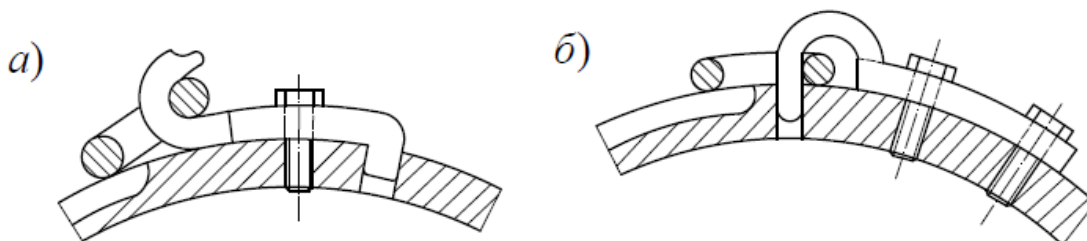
Крепление сварной цепи к барабану: *а* – кованым одноболтовым зажимом; *б* – двухболтовым зажимом
